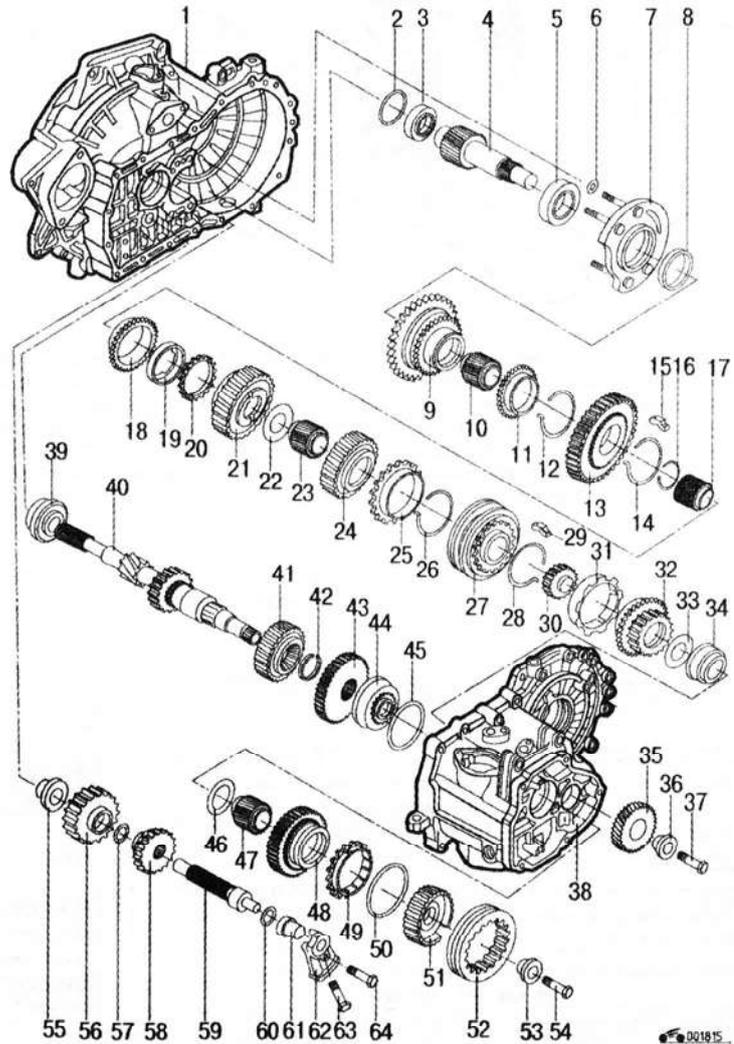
Вали и шестерни пятиступенчатой коробки передач: 1 – картер сцепления; 2 – регулировочная шайба; 3 – конический подшипник (малый); 4 – вторичный вал; 5 – конический подшипник (большой); 6 – шайба круглого сечения; 7 – опора подшипника; 8, 22, 33, 46, 60 – упорные шайбы; 9 – шестерня I передачи; 10, 23, 30, 47 – игольчатые подшипники; 11, 18, 25, 31, 49 – кольца синхронизаторов; 12, 14, 26, 28 – пружины; 13, 15, 29, 27 – синхронизаторы; 16, 17 – стопорные кольца игольчатого подшипника; 19 – внешнее кольцо синхронизатора; 20 – внутреннее кольцо синхронизатора; 21 – шестерня II передачи; 24 – шестерня III передачи; 32 – шестерня IV передачи; 34, 36, 53, 55, 61 – втулки; 35 – шестерня V передачи; 37, 54 – болты М8х26; 38 – картер коробки передач; 39 – роликовый подшипник; 40 – первичный вал; 41 – шестерня I передачи; 42 – стопорное кольцо; 43 – шестерня IV передачи; 44 – роликовый подшипник; 45 – регулировочное кольцо; 48 – шестерня V передачи; 50 – пружина; 51 – ступица синхронизатора; 52 – скользящая муфта синхронизатора; 56 – промежуточная шестерня; 57 – стопорное кольцо; 58 – шестерня передачи заднего хода; 59 – вал шестерни передачи заднего хода; 62 – держатель вала заднего хода; 63 – винт продольного крепления держателя; 64 – винт поперечного крепления держателя
